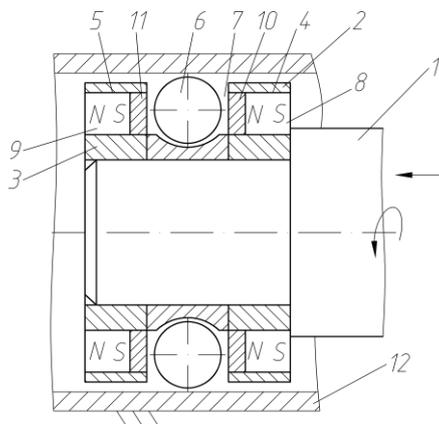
Схема магнитно-центробежного раскатывания внутренних поверхностей вращения
